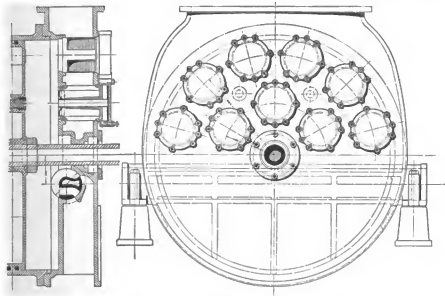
Windcylinder im raschlaufenden Gehäuse mit Gasmotorantrieb.
